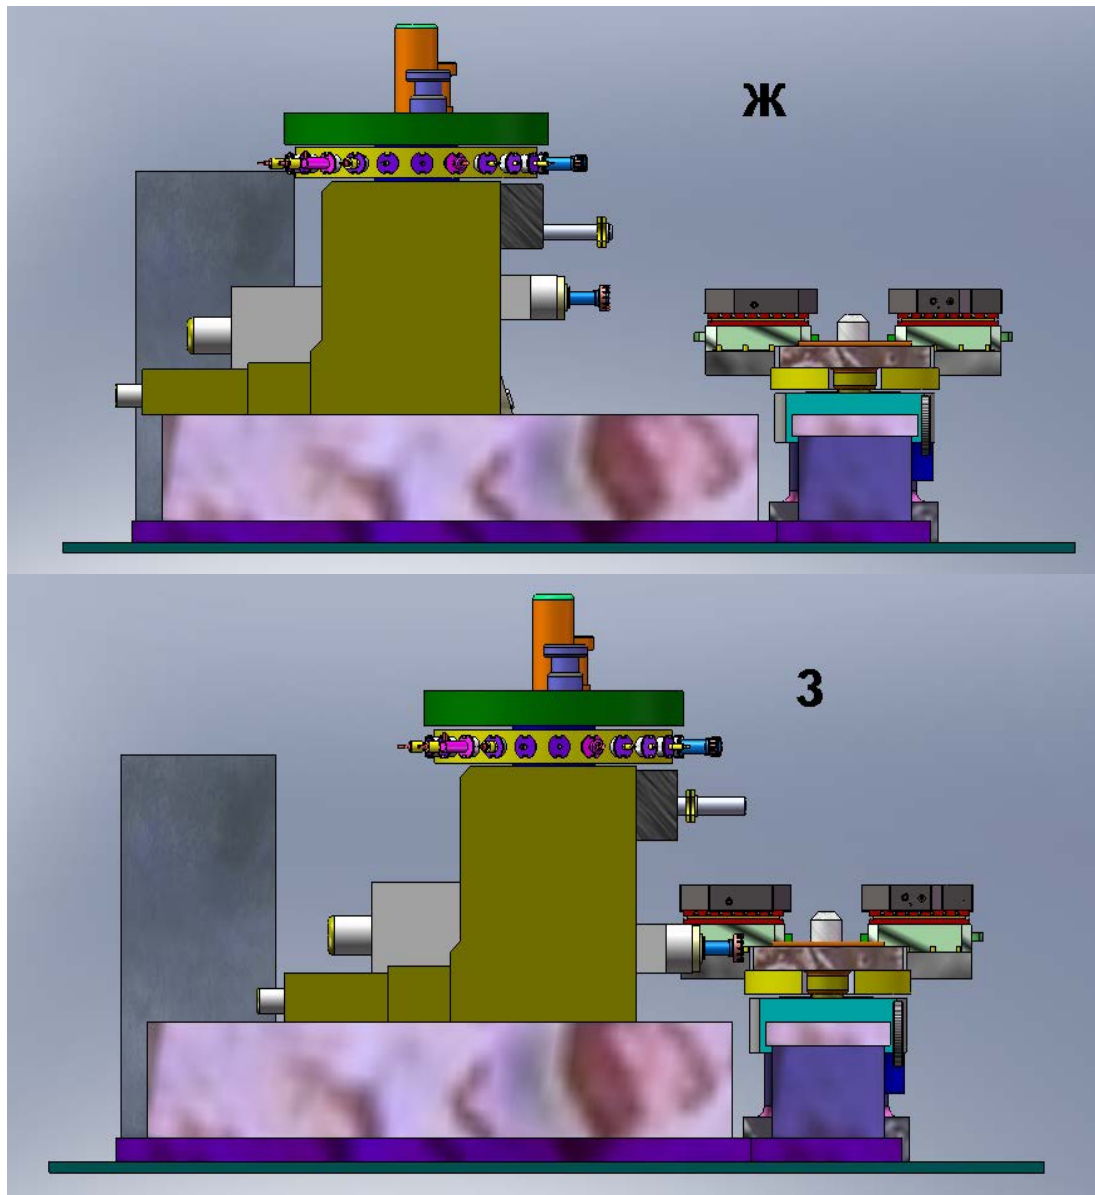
Положення основних вузлів обробного центру IP500ПМФ4
